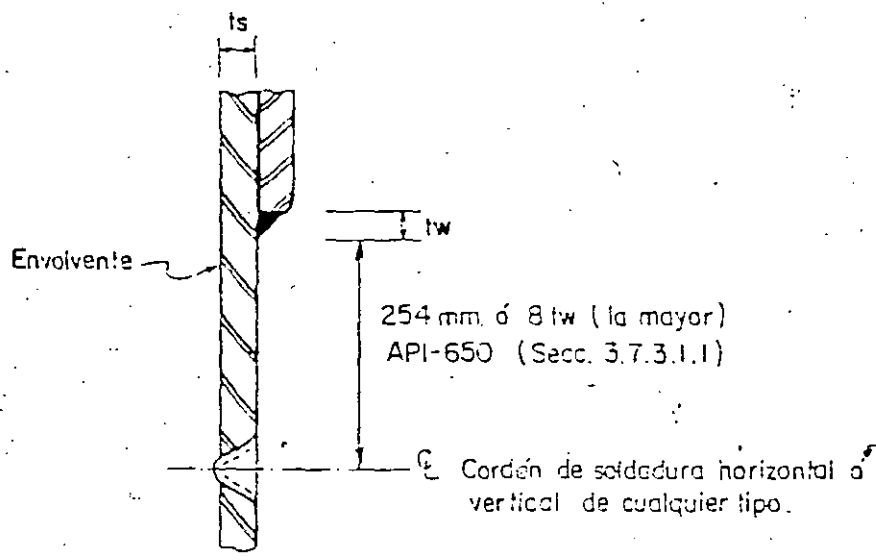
Espaciamiento mínimo entre accesorios de la envolvente y cordones de soldaduras a tope de cualquier tipo.
